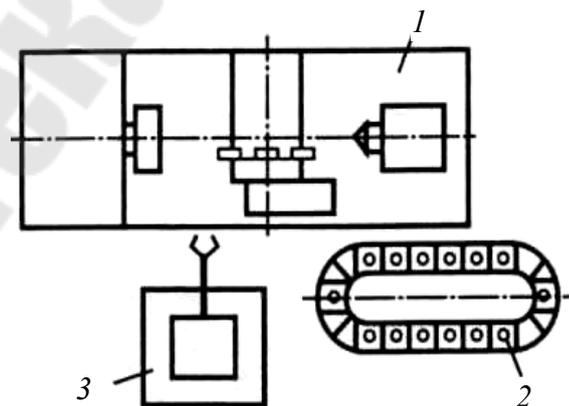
Компоновка робототехнического комплекса: 1 – токарный полуавтомат модели 16К20Ф3; 2 – тактовый стол (накопитель заготовок и деталей); 3 – промышленный робот модели М20П.40.01 (рис. 5.9)
